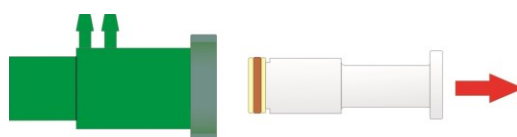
Montagewerkzeug mit Verwirbelungskörper herausziehen
